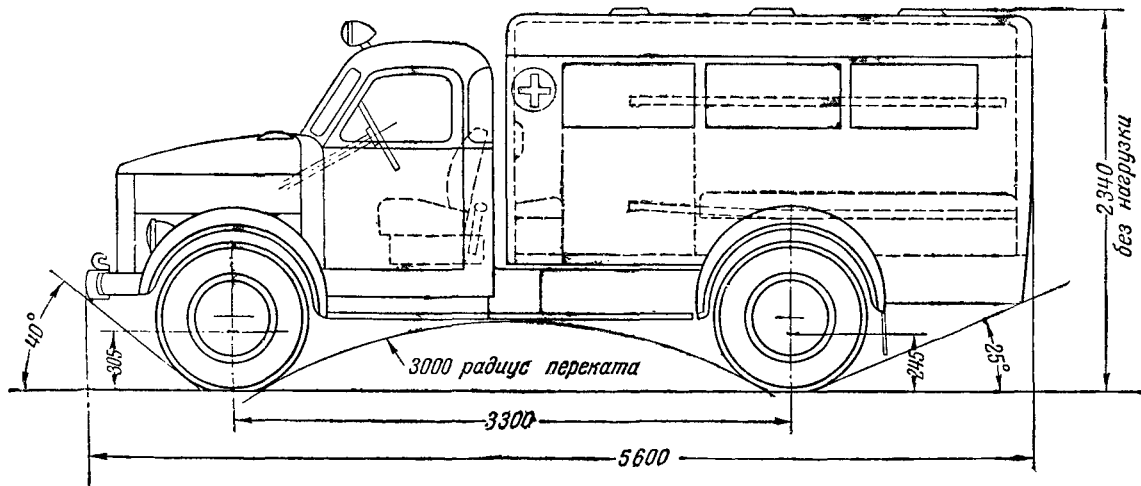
Схема санитарного автомобиля ПАЗ-653.
